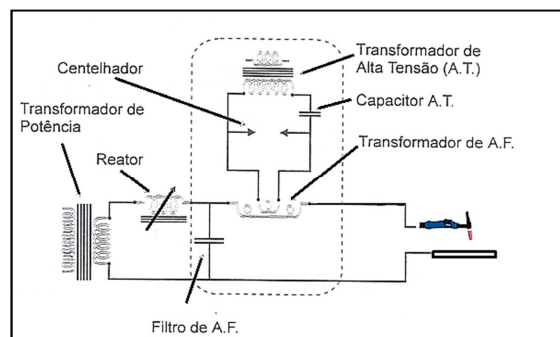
Esquema de máquina de solda com transformador convencional com unidade centelhadora (alta-frequência) (Adaptado de Welding Institute RWTH, Aachen University, Welding Technology Welding and Cutting Technologies).
